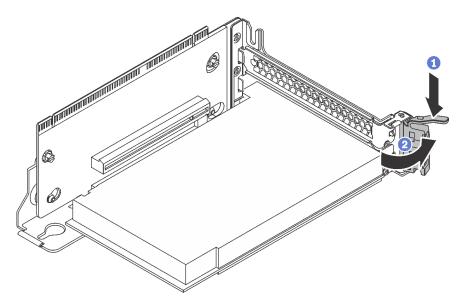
Apertura del mecanismo de cierre de sujeción del adaptador PCIe
